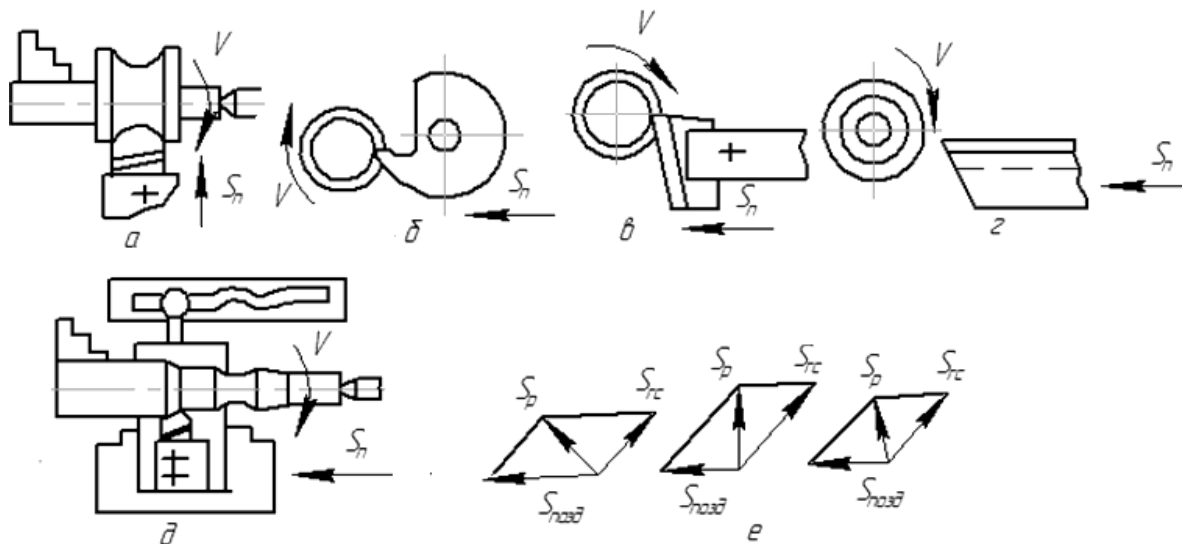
Схеми обробки фасонних поверхонь на токарно-гвинторізних верстатах
